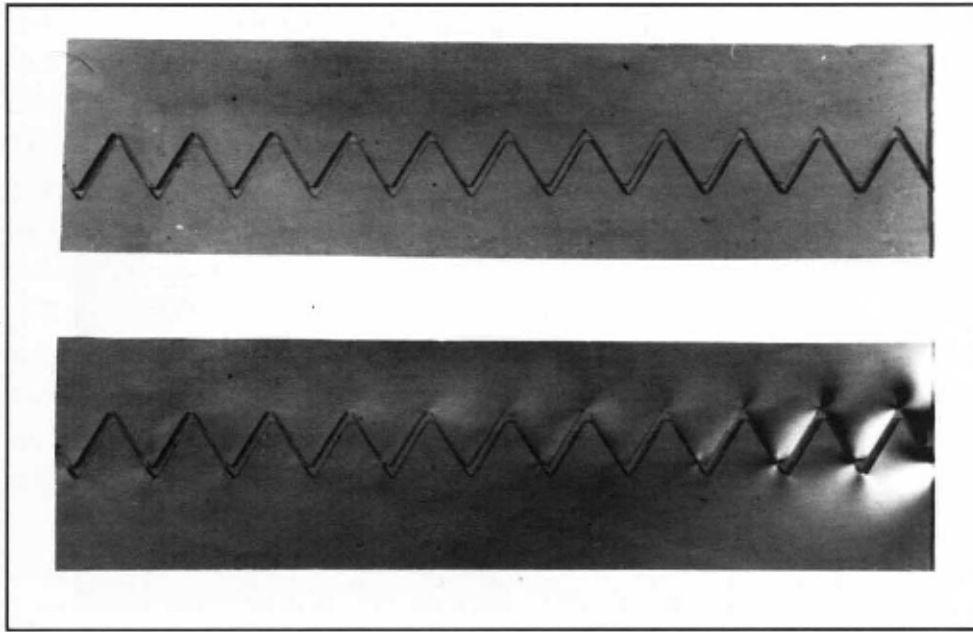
Фотография пластиковой модели резьбы соединения ствола (стандартная V-образная резьба), использующая поляризованный свет. Демонстрируется нагрузка концентрируется на первых нескольких витках резьбы около передней части ресивера (снизу справа). На верхнем фото показана резьба в ненагруженных условиях.
